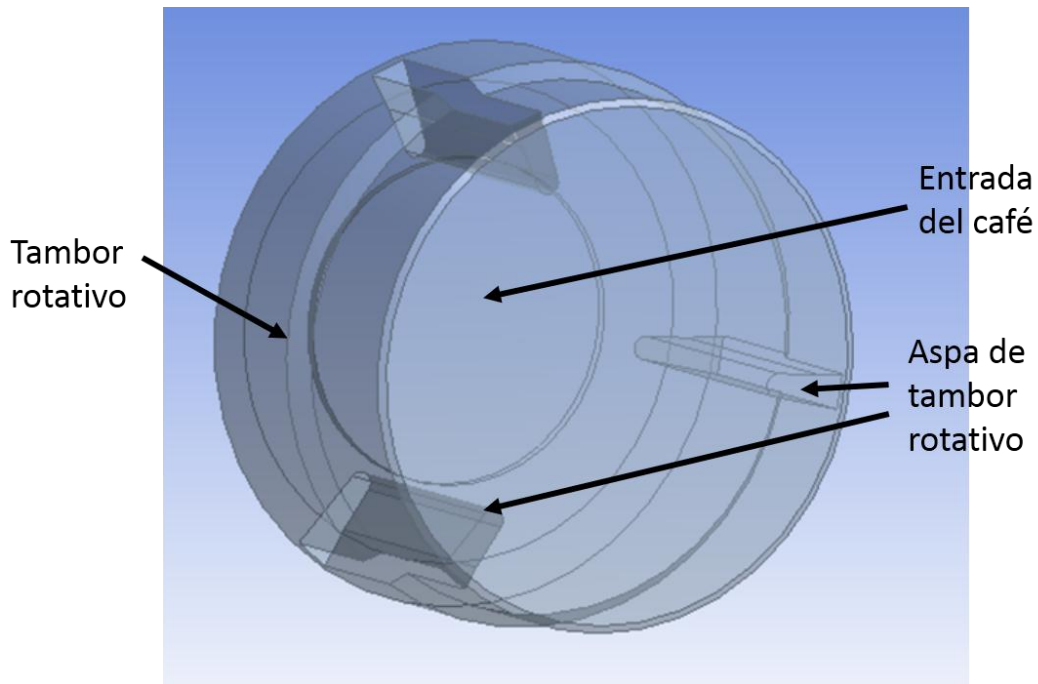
Ensamble del Tambor rotativo Fuente: Autor
